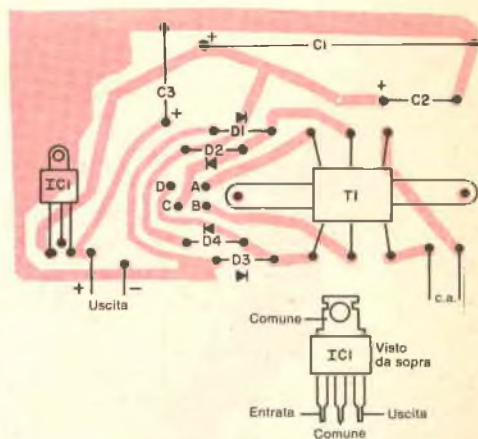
Circuito stampato, nella figura in alto, e disposizione dei componenti (figura di destra). Per il montaggio di IC1 si veda il testo.
